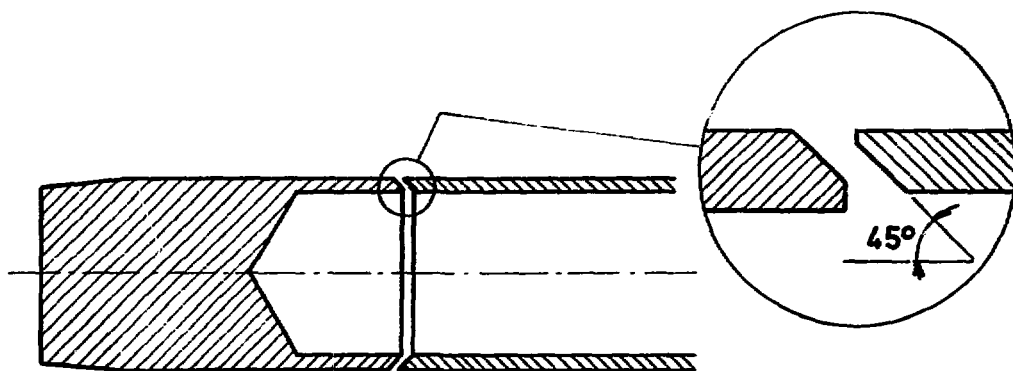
SOUDURE EN BOUT A ACCOSTAGE CONIQUE
